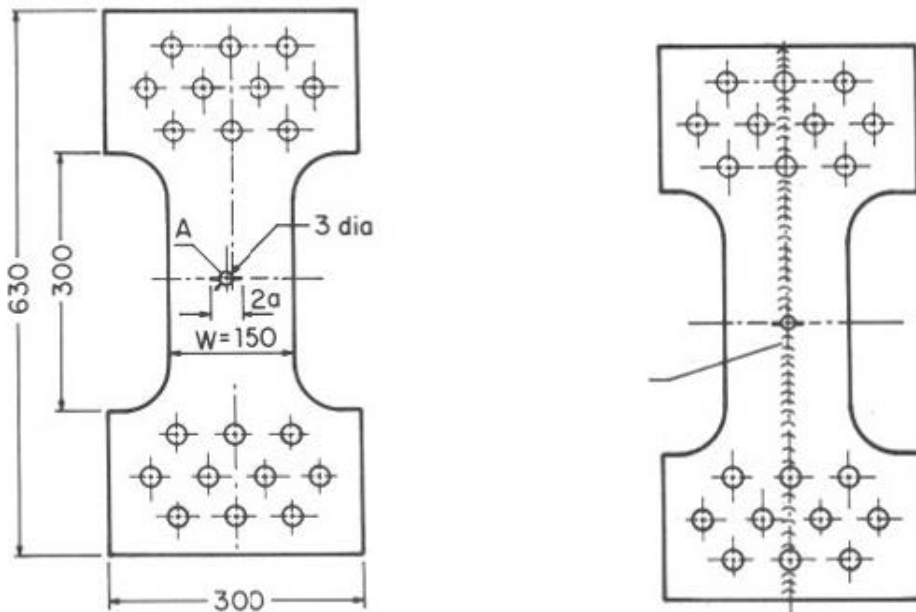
Formes et dimensions d'éprouvettes soudées longitudinalement
